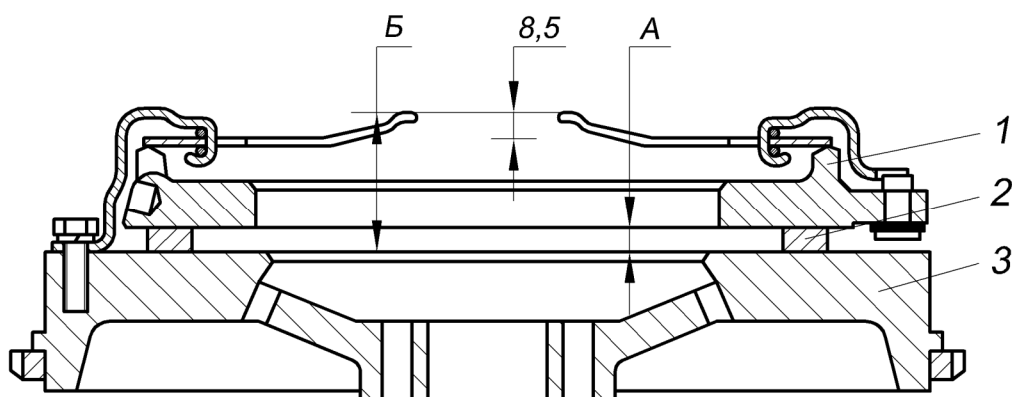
Регулировка концов лепестков и проверка нажимного диска сцепления:
